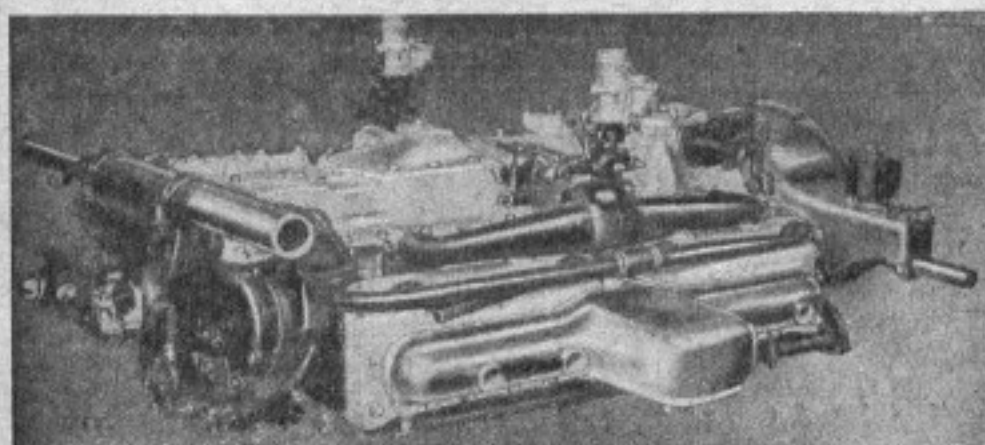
Общий вид двигателя Уайт, модель 10-А
